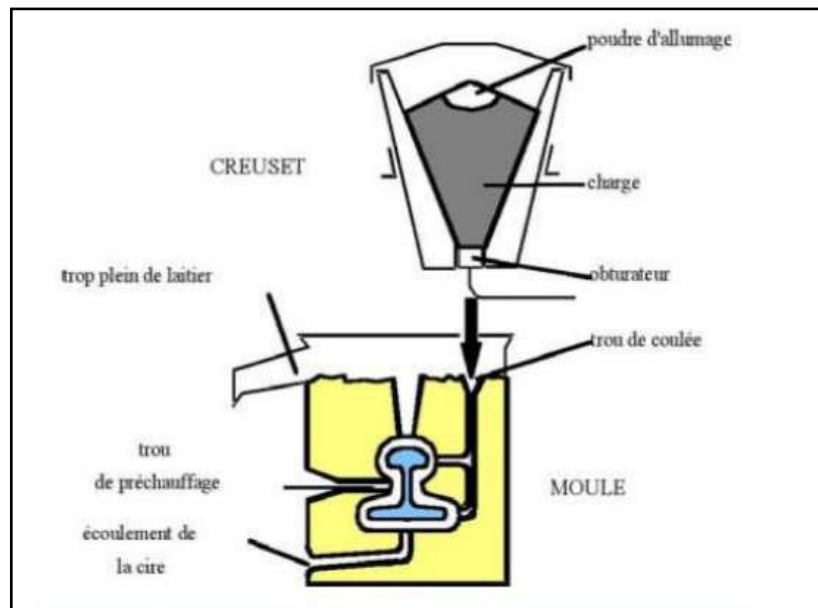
Schéma illustrant le procédé de soudage aluminothermique
